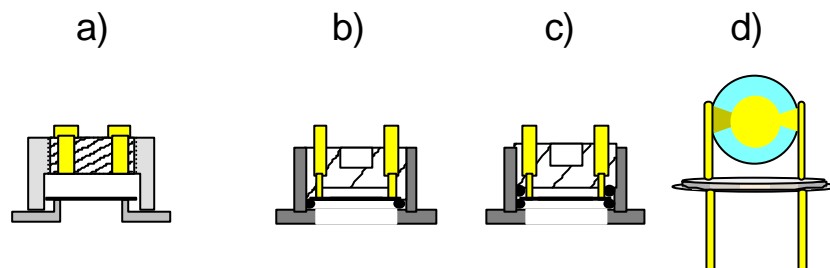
Verschiedene Versionen von Schwingquarzhaltern: a) abgekapselter Chip mit aufgeklebtem Quarz, b) abgekapselter Chip mit einfacher O-Ring-Pressung, c) abgekapselter Chip mit doppelter O-Ring-Pressung, d) Quarzhalter für die Gasphase.
